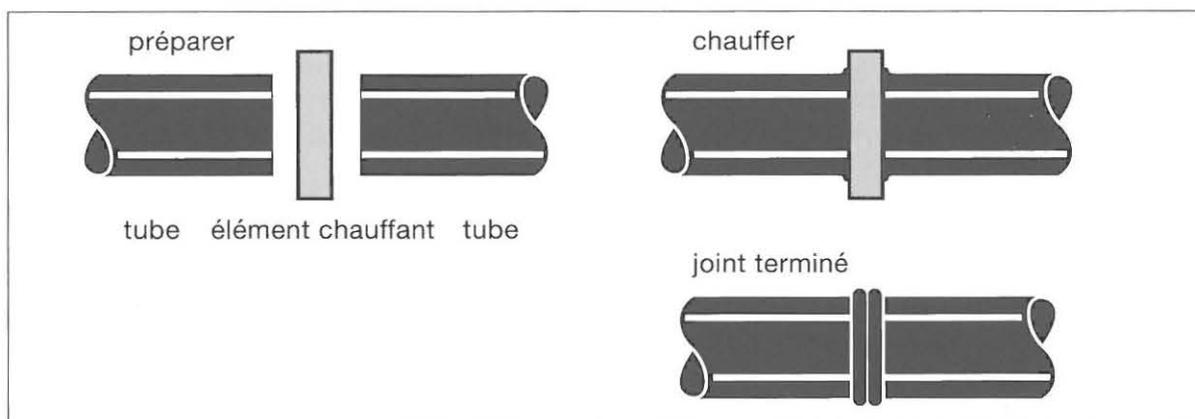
Principe du soudage bout-à-bout
